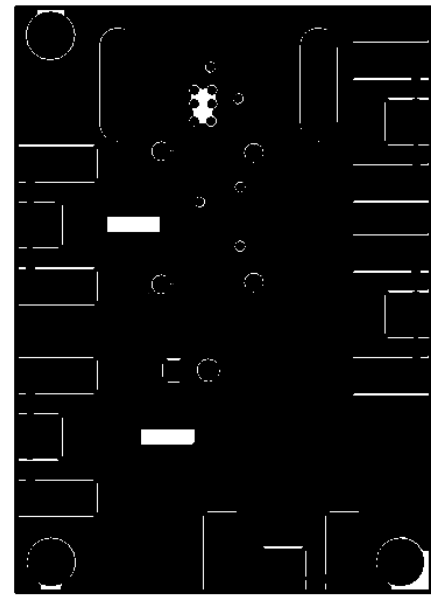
MAX3744/MAX3745 评估板 PCB 布线
